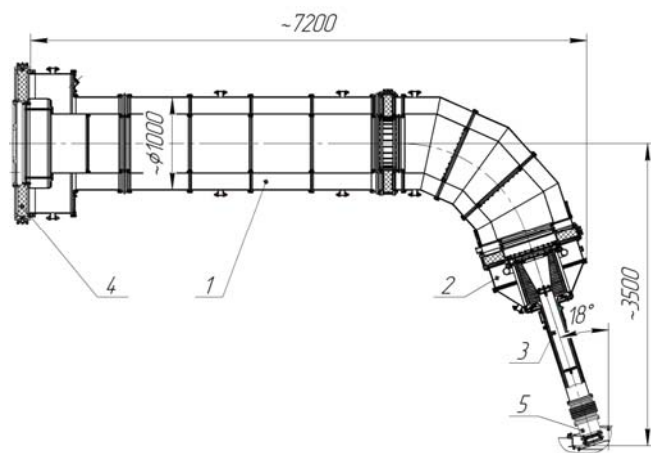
Конструктивная схема СПЭ типового модуля установки «Гамма-4»: 1 – ВПЛ; 2 – УТ; 3 – МИПЛ; 4 – опорный изолятор СФВИ; 5 – вакуумная камера с диодной нагрузкой
